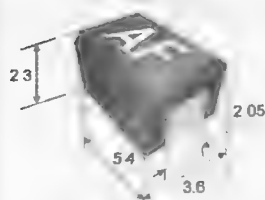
Внешний вид и размеры корпуса DO-214AA
